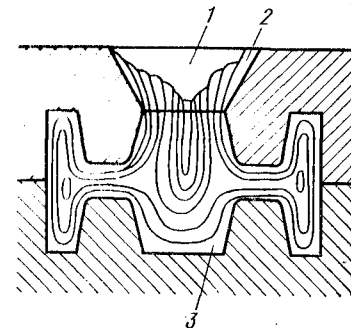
Схема образования усадочной раковины в прибыльной части отливки:
